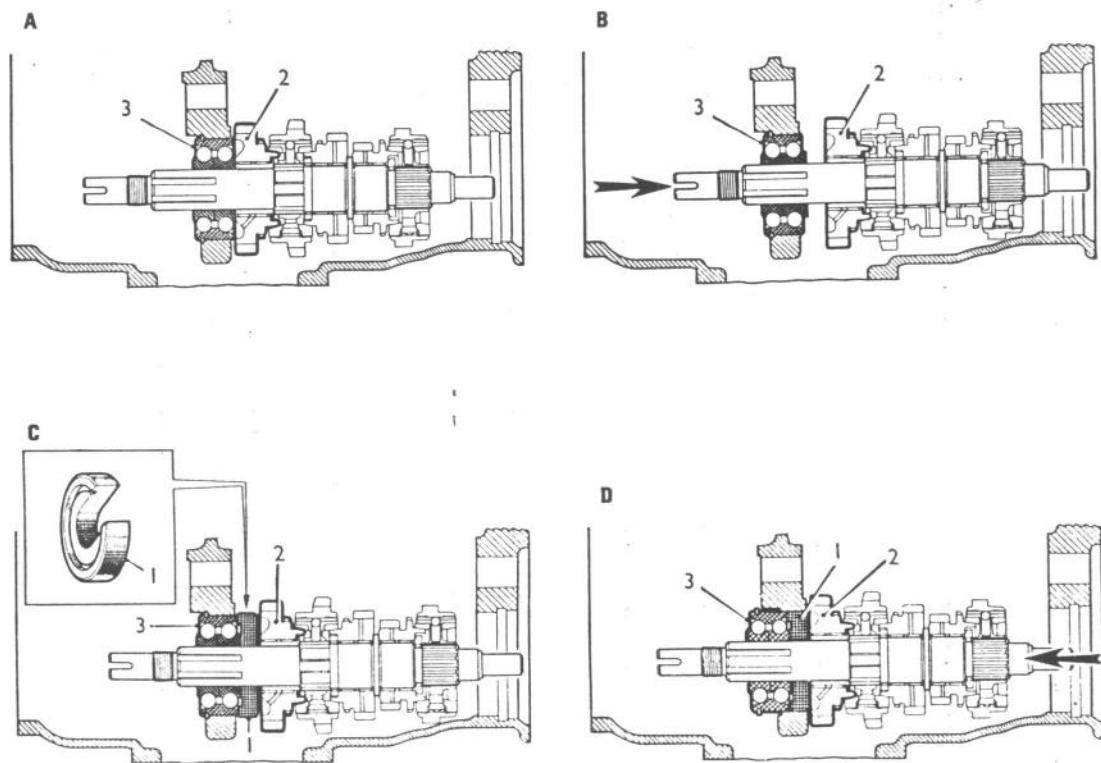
Modo de extraer el rodamiento del eje de salida de la caja de cambios, mediante el empleo de útil 18 G 1127.
